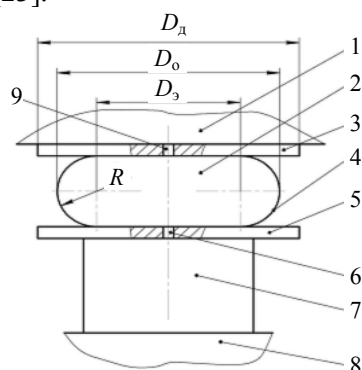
Пневморессора с повышенным демпфированием колебаний: 1 – кузов транспортного средства; 2 – пневморессора; 3, 5 – днище; 4 – гибкая оболочка; 6 – дроссельное отверстие; 7 – дополнительный резервуар; 8 – рама тележки; 9 – отверстие для питания пневморессоры сжатым воздухом
